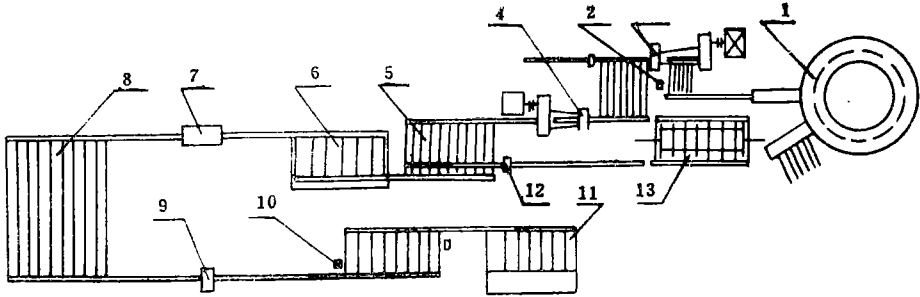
衡阳钢管厂三辊轧管机组设备平面布置图
